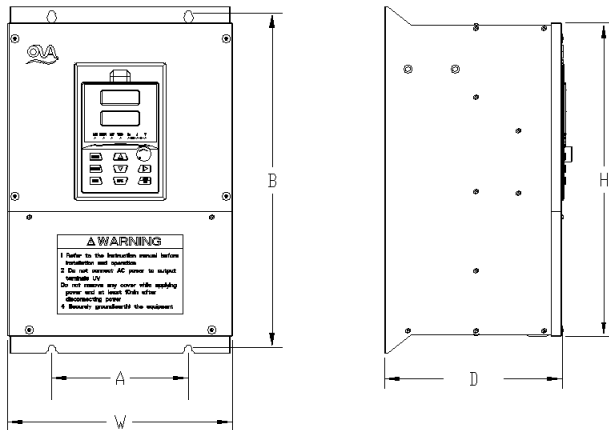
EM600系列金属机箱结构外型尺寸及安装尺寸示意图
